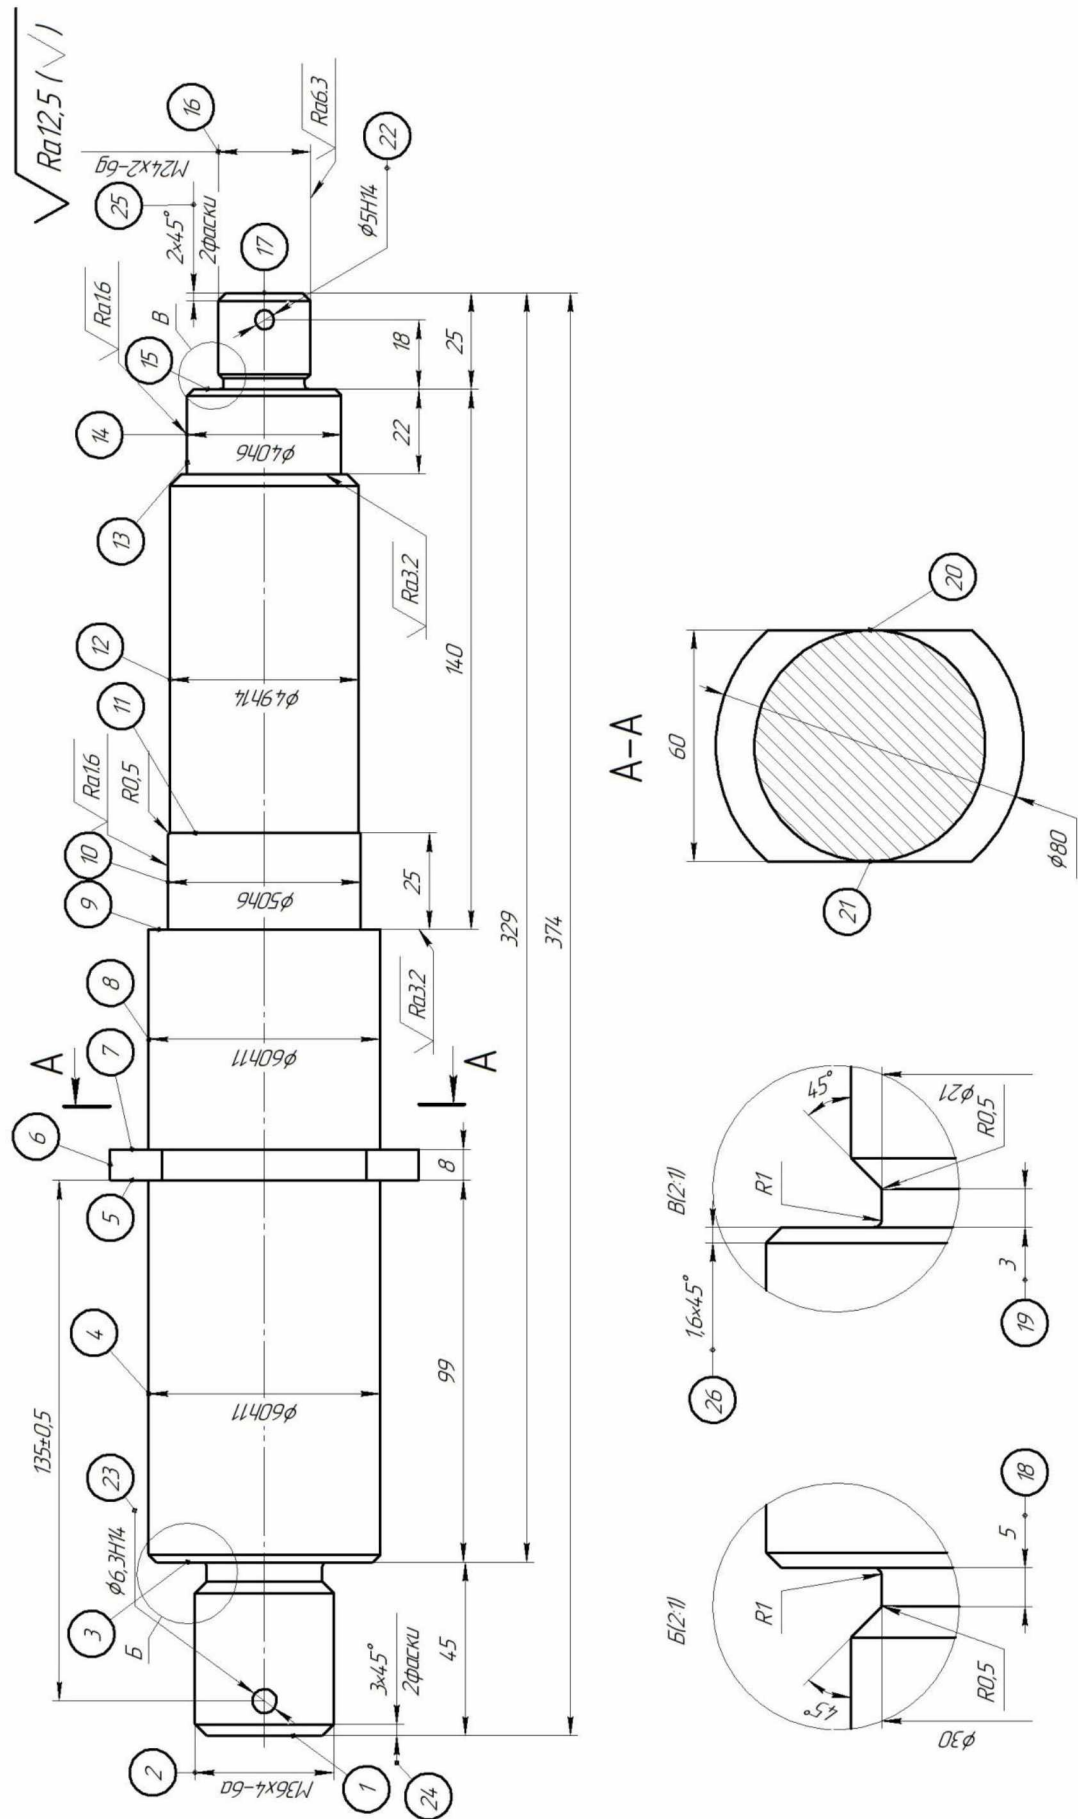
Нумерація поверхонь деталі «Вісь»
